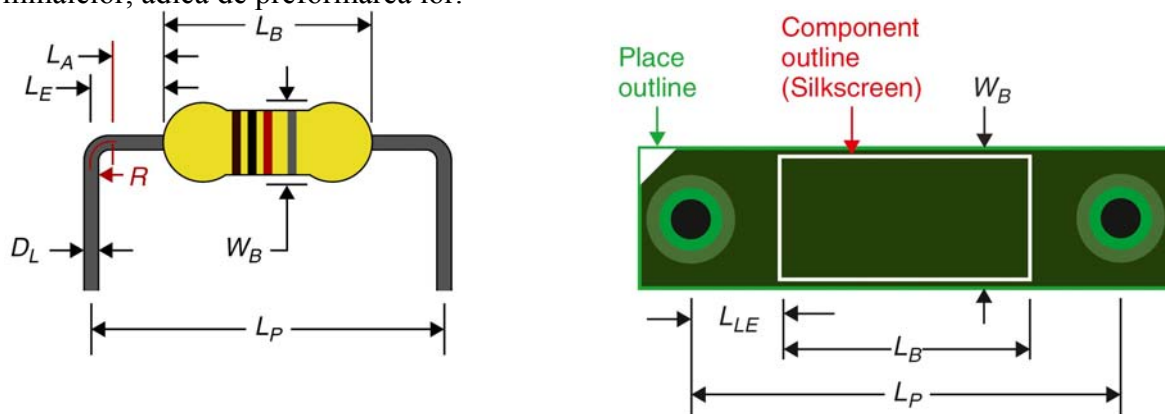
Componentă cu terminale axiale b) mod de reprezentare în Layout
